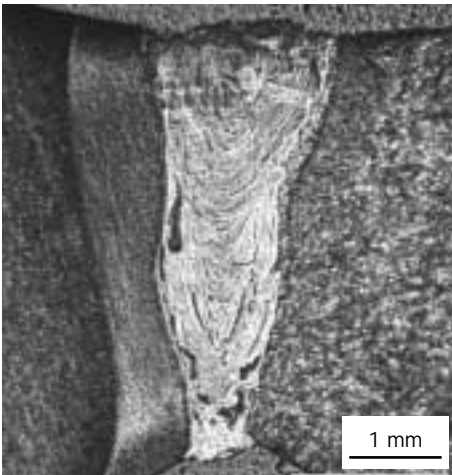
Typische Schweißnaht eines Bauteils aus dem Getriebebau
